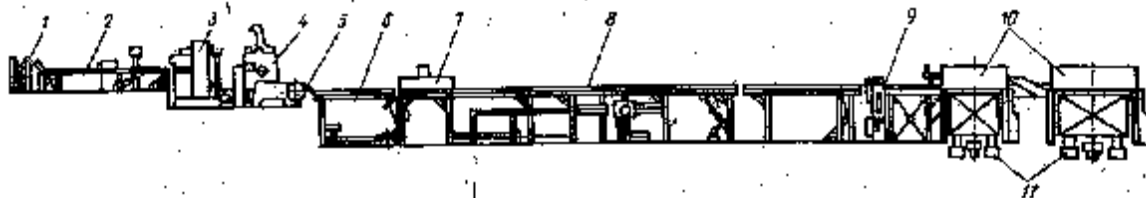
Схема полуавтоматической линии ЛУР-3: 1 - продольный конвейер подачи чураков, 2 - накопитель чураков, 3- центровочно-загрузочное устройство, 4 - лущильный станок ЛУ-17-10, 5 - поворотный роликовый конвейер, 6 - приемный конвейер, 7 - ножжевая рамка, 8 - конвейер - петлеукладчик, 9- ножницы для рубки шпона, 10 - укладчик шпона, 11 - конвейеры вывоза стоп.
